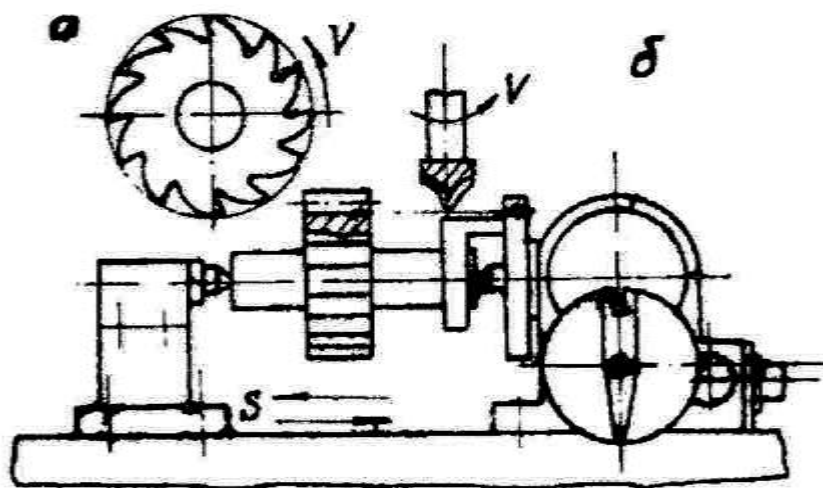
Фрезерование прямозубых цилиндрических зубчатых колес модульными фрезами:
